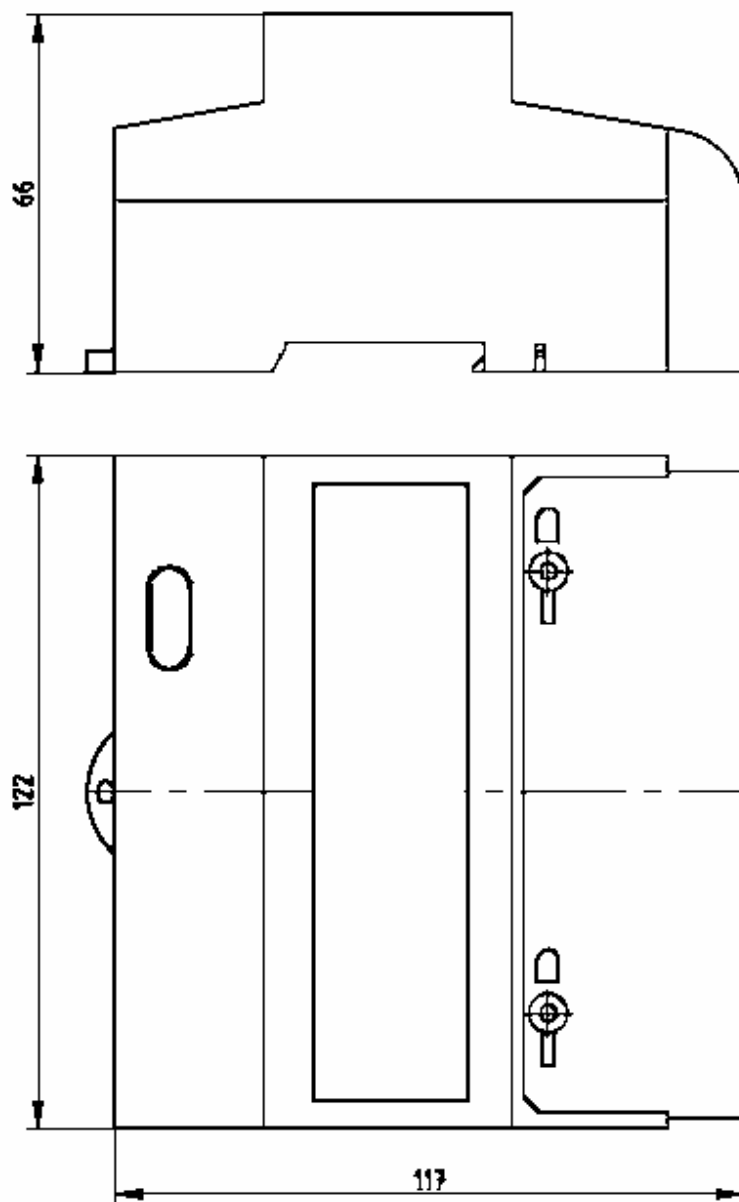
Габаритный чертеж счетчика электрической энергии трехфазного СЭТ3а-02-64-05-Ш-Д
